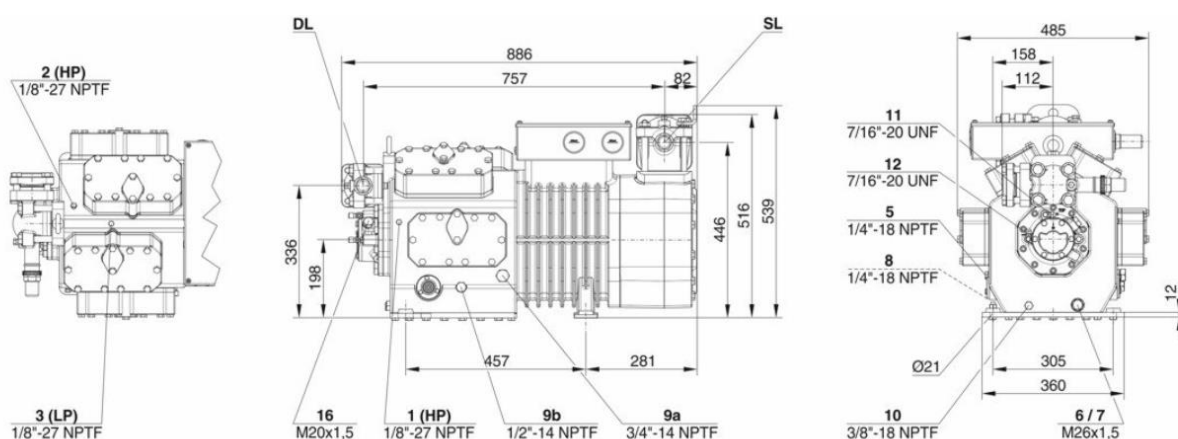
Поршневий компресор 8GE-60Y-40P [8]
